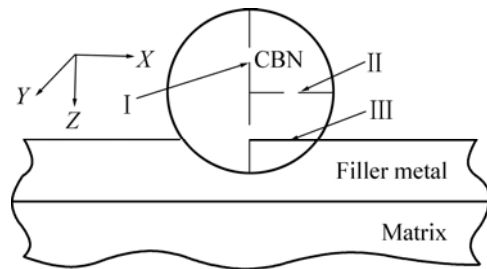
钎焊 CBN 磨粒试样结构示意图
